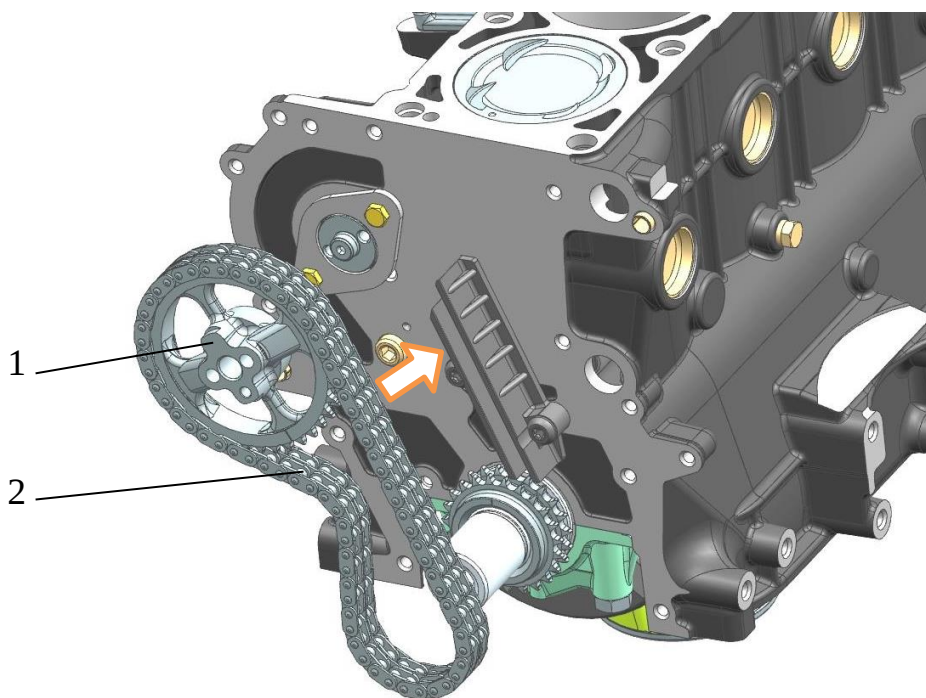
Установка нижней цепи с ведомой звездочкой промежуточного вала:
